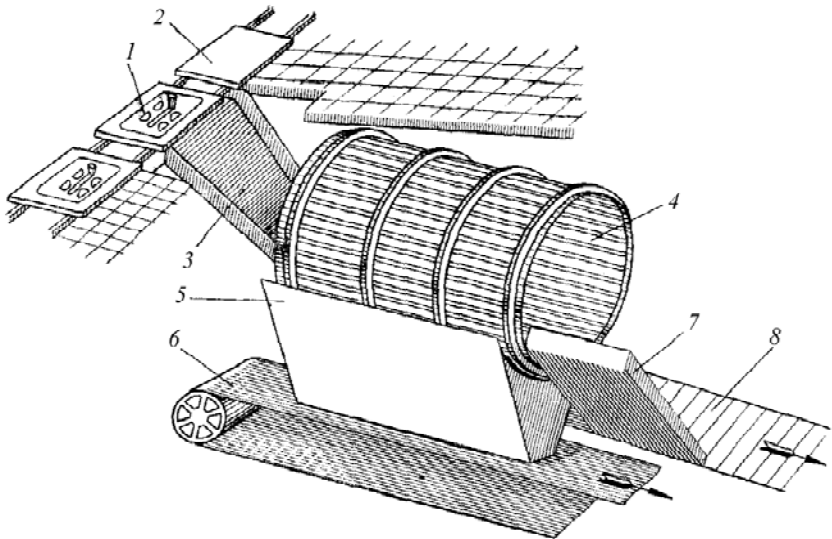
Схема установки для вибивання виливків із оболонкових форм:
